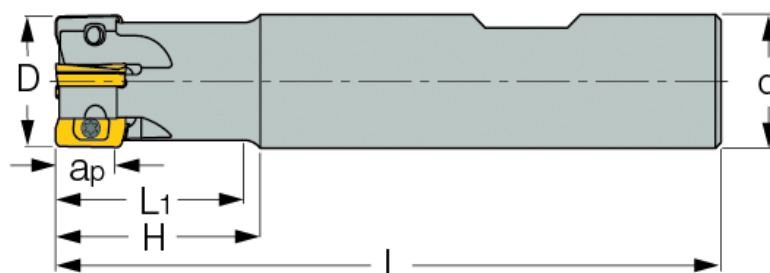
Корпус фрезы HP E90AN D20-4-C20-07-C
